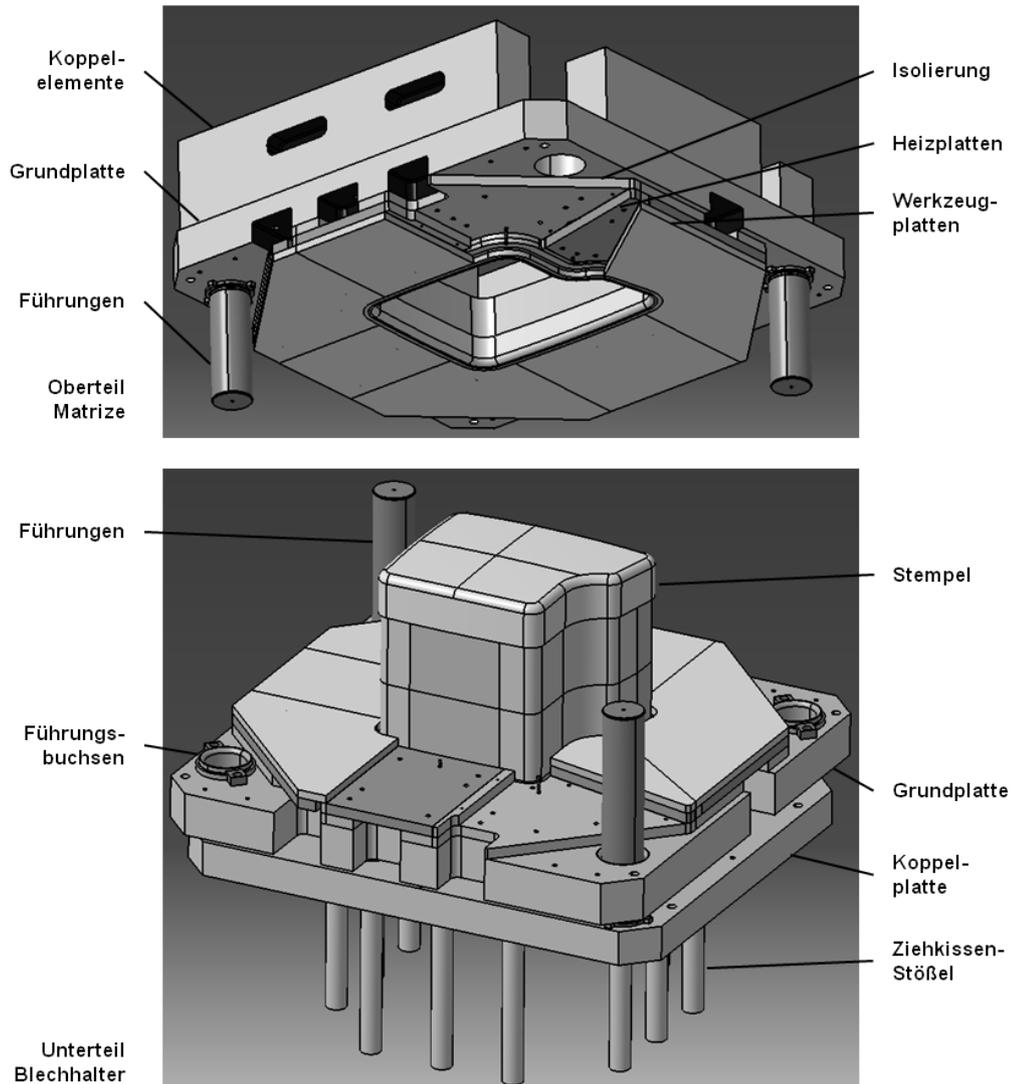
CAD-Modell des Prototypenwerkzeugs
